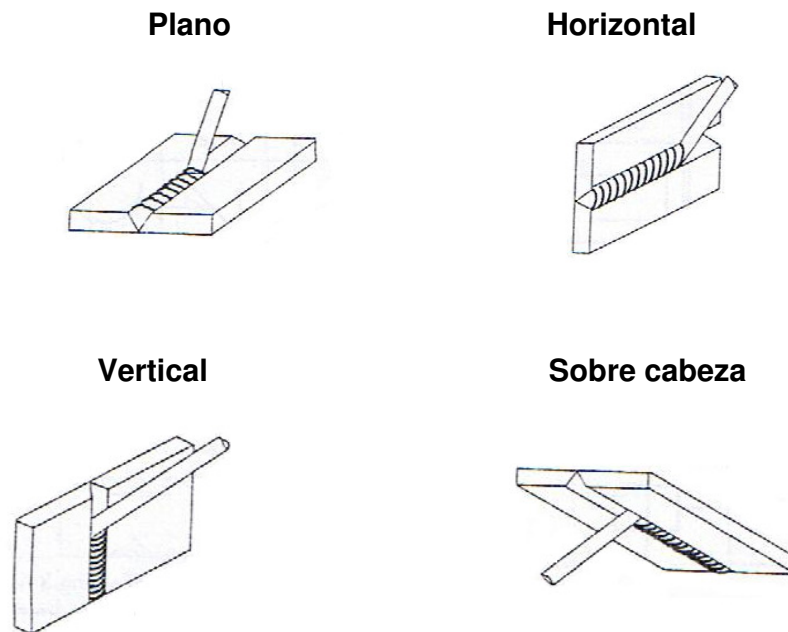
Posiciones de soldadura del S.A.P.⁶
